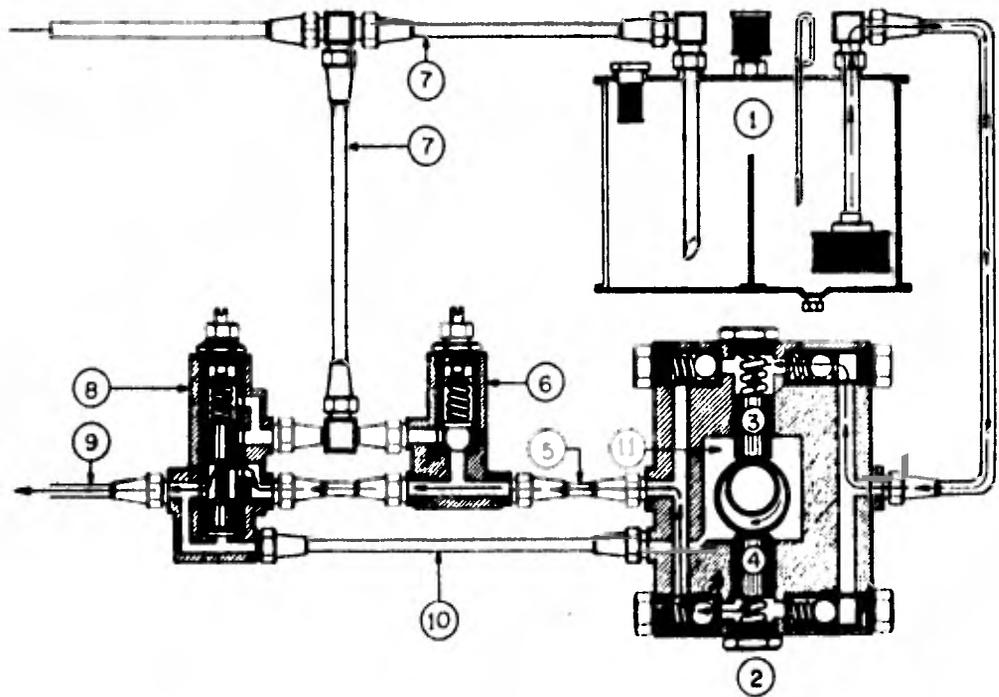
Conjunto de bomba y válvulas de presión.
